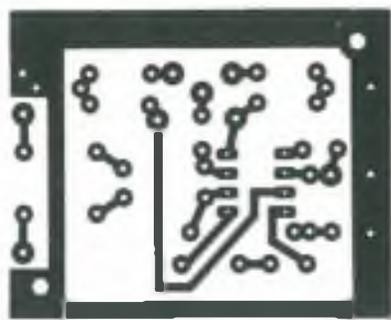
Disegno del circuito stampato Scala 1:1 su cui è montato il cardiografo. Notare le piccole dimensioni dell'apparecchio.
